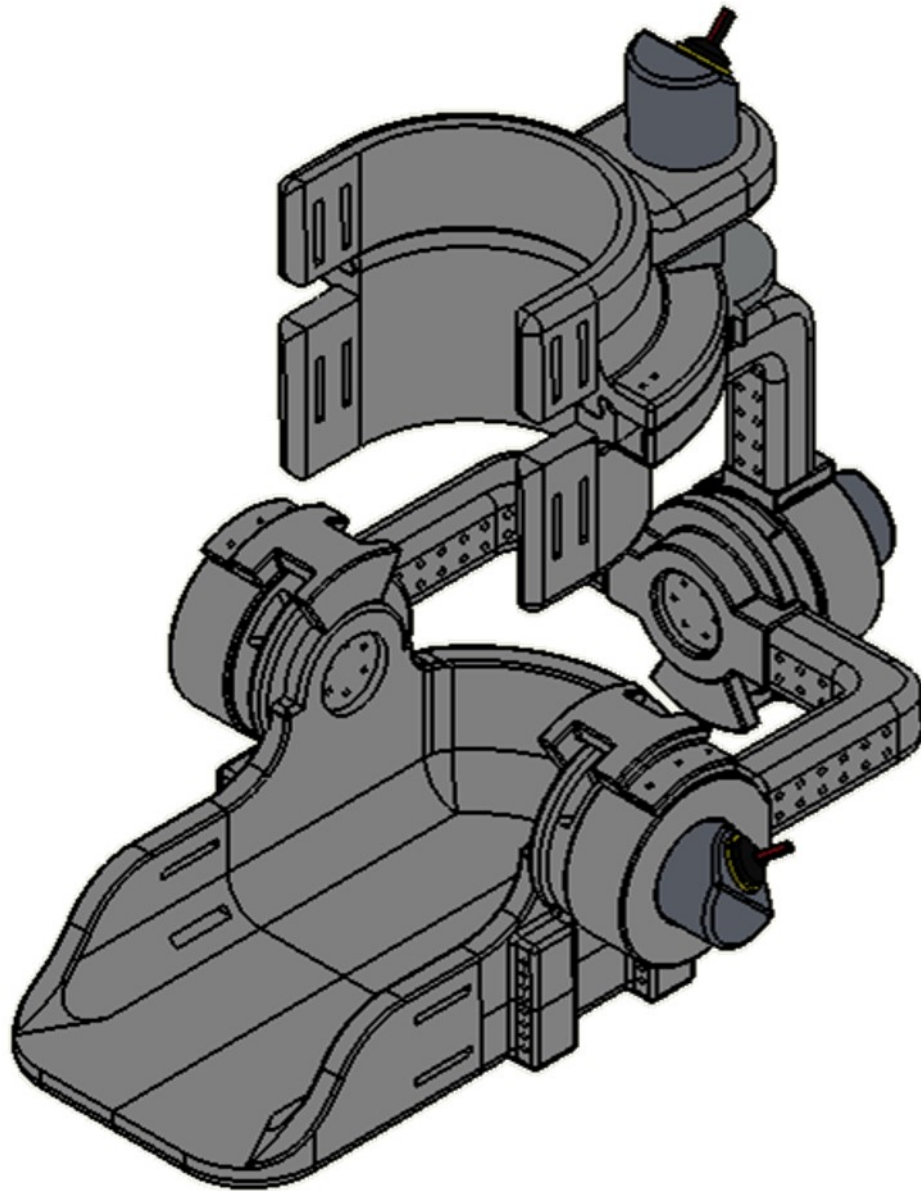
Ensamble completo de órtesis pasiva con vista isométrica.
